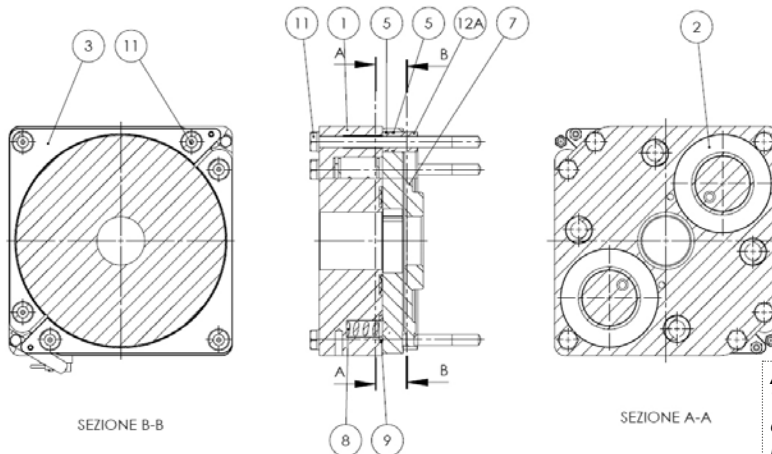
Explosionszeichnung der Bremse DFX3.
